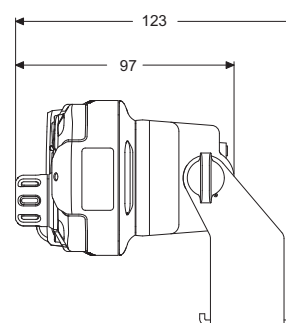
Vista Lateral da Cabeça de Controle O2 com Munhão e Montagem Remota
